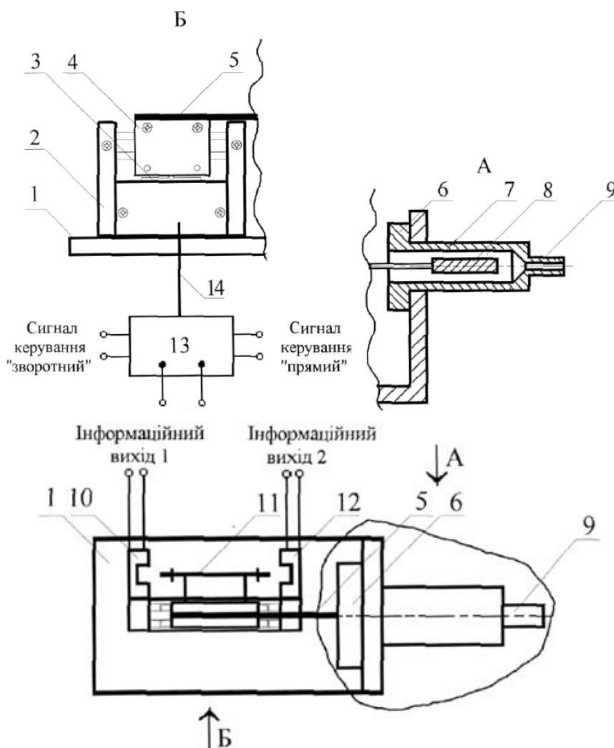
П'єзоелектричний віскозиметр: 1 – основа; 2 – реверсивний лінійний п'єзоелектричний двигун; 3 – осцилятор двигуна; 4 – рухома частина; 5 – напрямна; 6 – вимірювальний зонд; 7 – вимірювальна камера; 8 – поршень; 9 – штуцер; 10, 12 – оптичні датчики; 11 – шторка; 13 – перетворювач напруги; 14 – кабель
